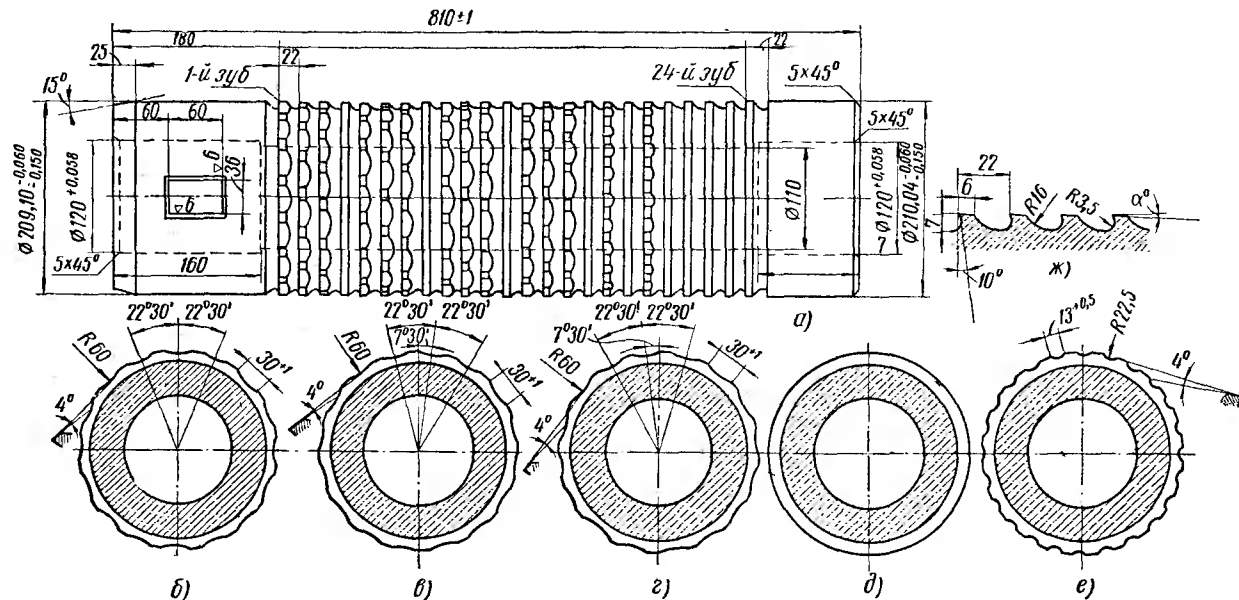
Круглая протяжка для отверстий большого диаметра:
